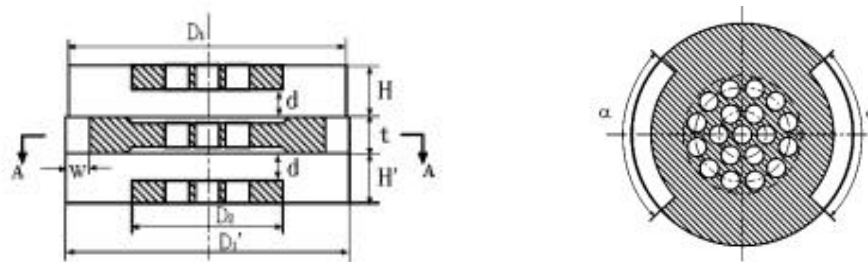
Конструкция двухзазорного резонатора для рассматриваемого клистроны [7]
